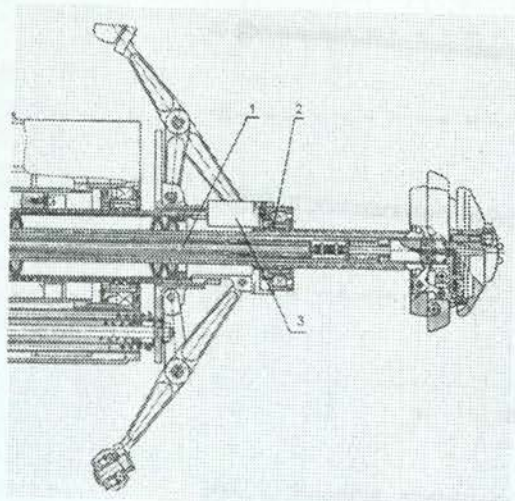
Стыковочный механизм: 1 — штанга; 2 — шарико-винтовой преобразователь; 3 — демпфер
